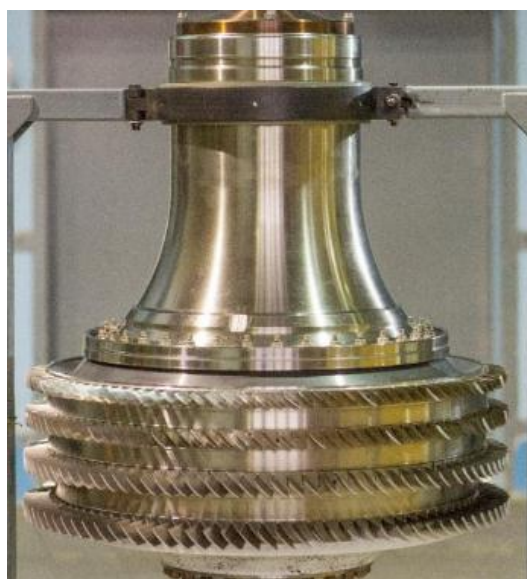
Сварной барабан ротора КВД из сплава ВЖ172
